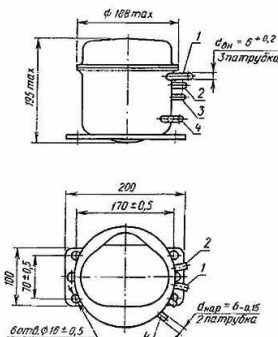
Общий вид кривошипно-кулисного мотор-компрессора: 1 — нагнетательный патрубок; 2 — операционный патрубок; 3 — всасывающий патрубок; 4 — патрубки устройства для дополнительного охлаждения
